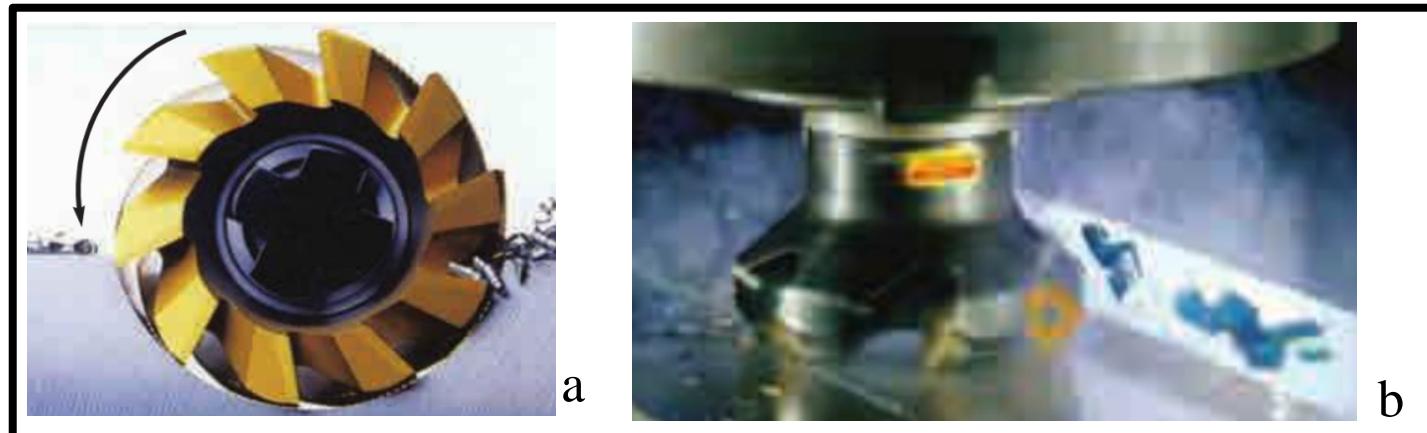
Operazione di fresatura: a) periferica; b) frontale
